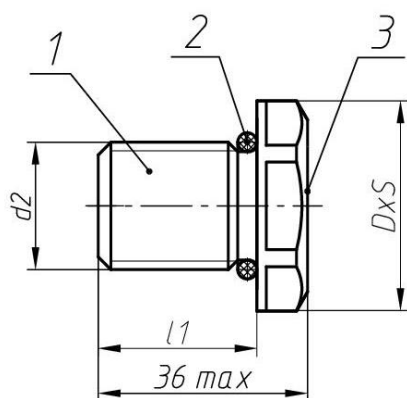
ExdKBU-M с соединителем металлоруква Герда-СГ с внутренней резьбой. Размеры см в таблице А.8
